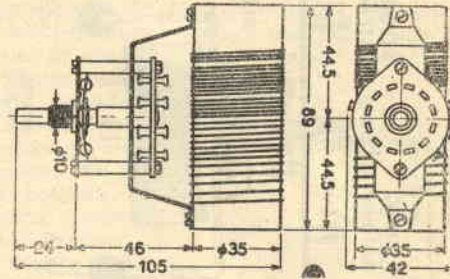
Dimensioni d'ingombro della bobina per stadio finale GELOSO N. 4/110.
